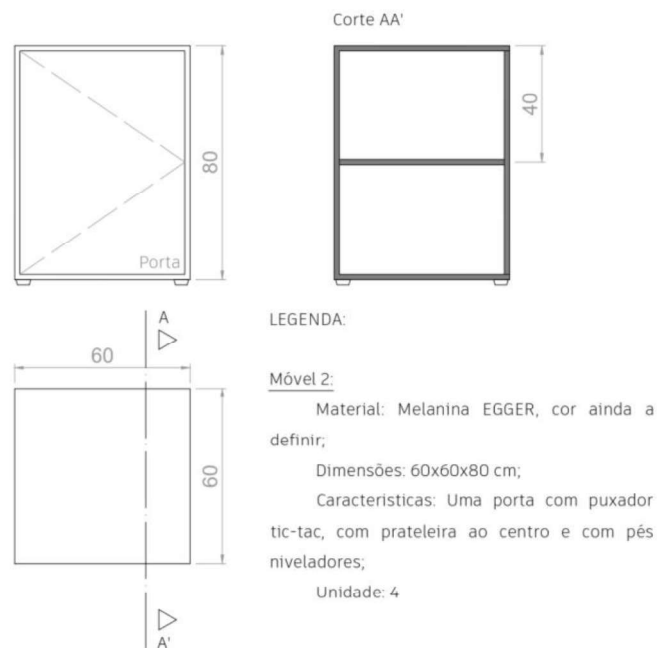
Desenho técnico de produção, módulo 2. Fonte: Autor
